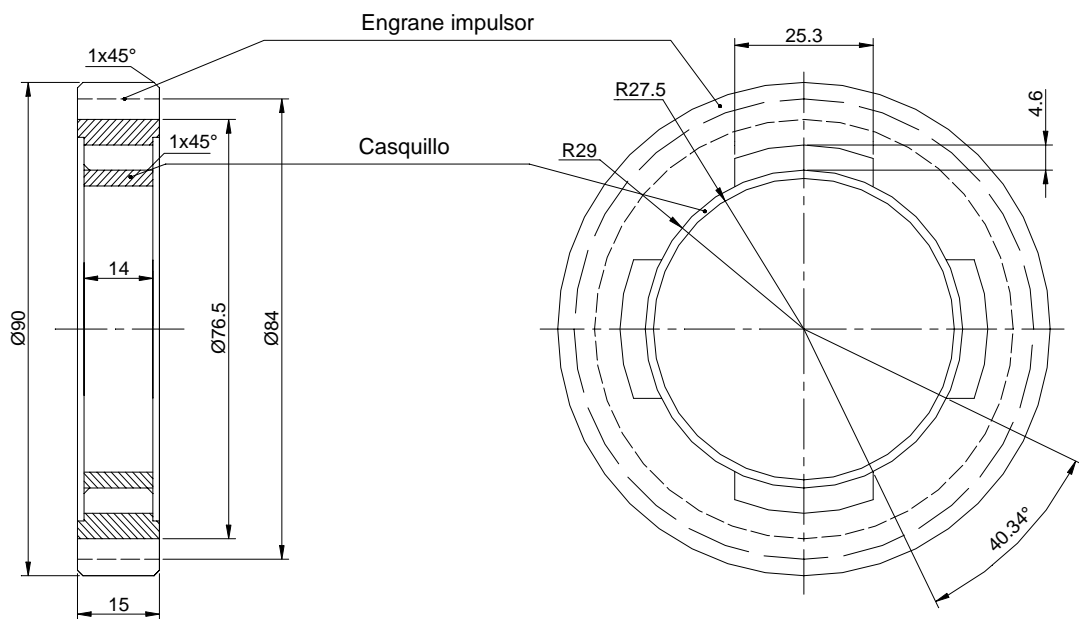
Esquema y dimensiones del montaje del casquillo del cojinete en el interior del engrane impulsor.
